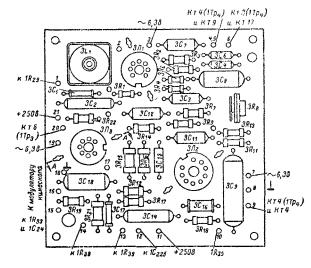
Расположение деталей на печатной плате задающего генератора и АПЧиФ строчной развертки телевизоров «Рубин-110» и «Рубин-111».
